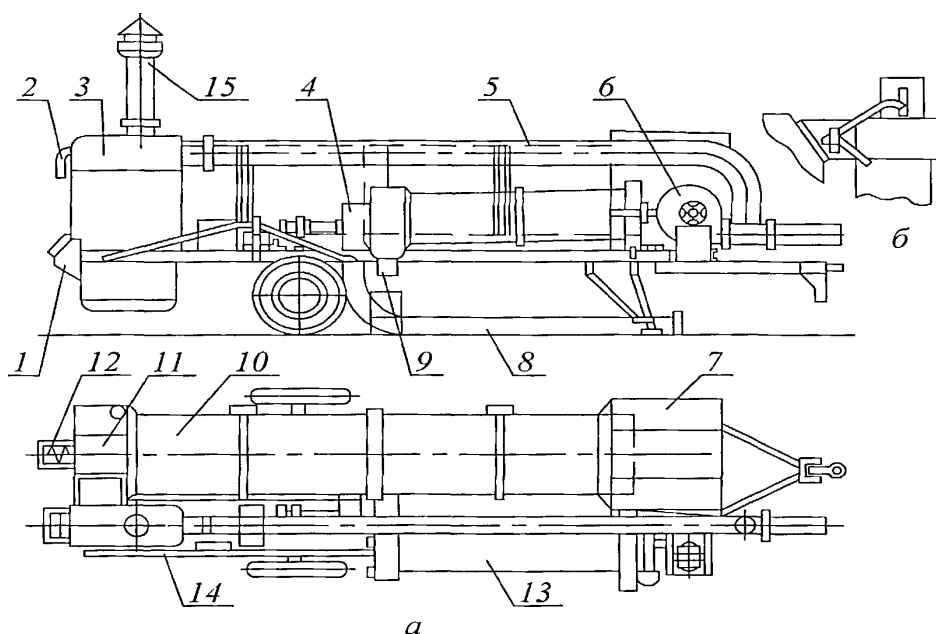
Пересувна барабанна сушарка СЗПБ– 2,5: а – схема сушарки; б – блокування дросель - клапанів. 1 – топка; 2 – патрубок регульованої подачі повітря; 3 – коробка змішувача; 4 – вентилятор охолодження; 5 – трубопровід; 6 – вентилятор сушильного барабана; 7 – задня камера; 8 – повітропроводи; 9 – шлюзовий затвор; 10– сушильний барабан; 11 – передня камера; 12 – бункер з шнеком; 13 – охолоджувальний барабан; 14 – рама з колісним ходом; 15 – димар.
